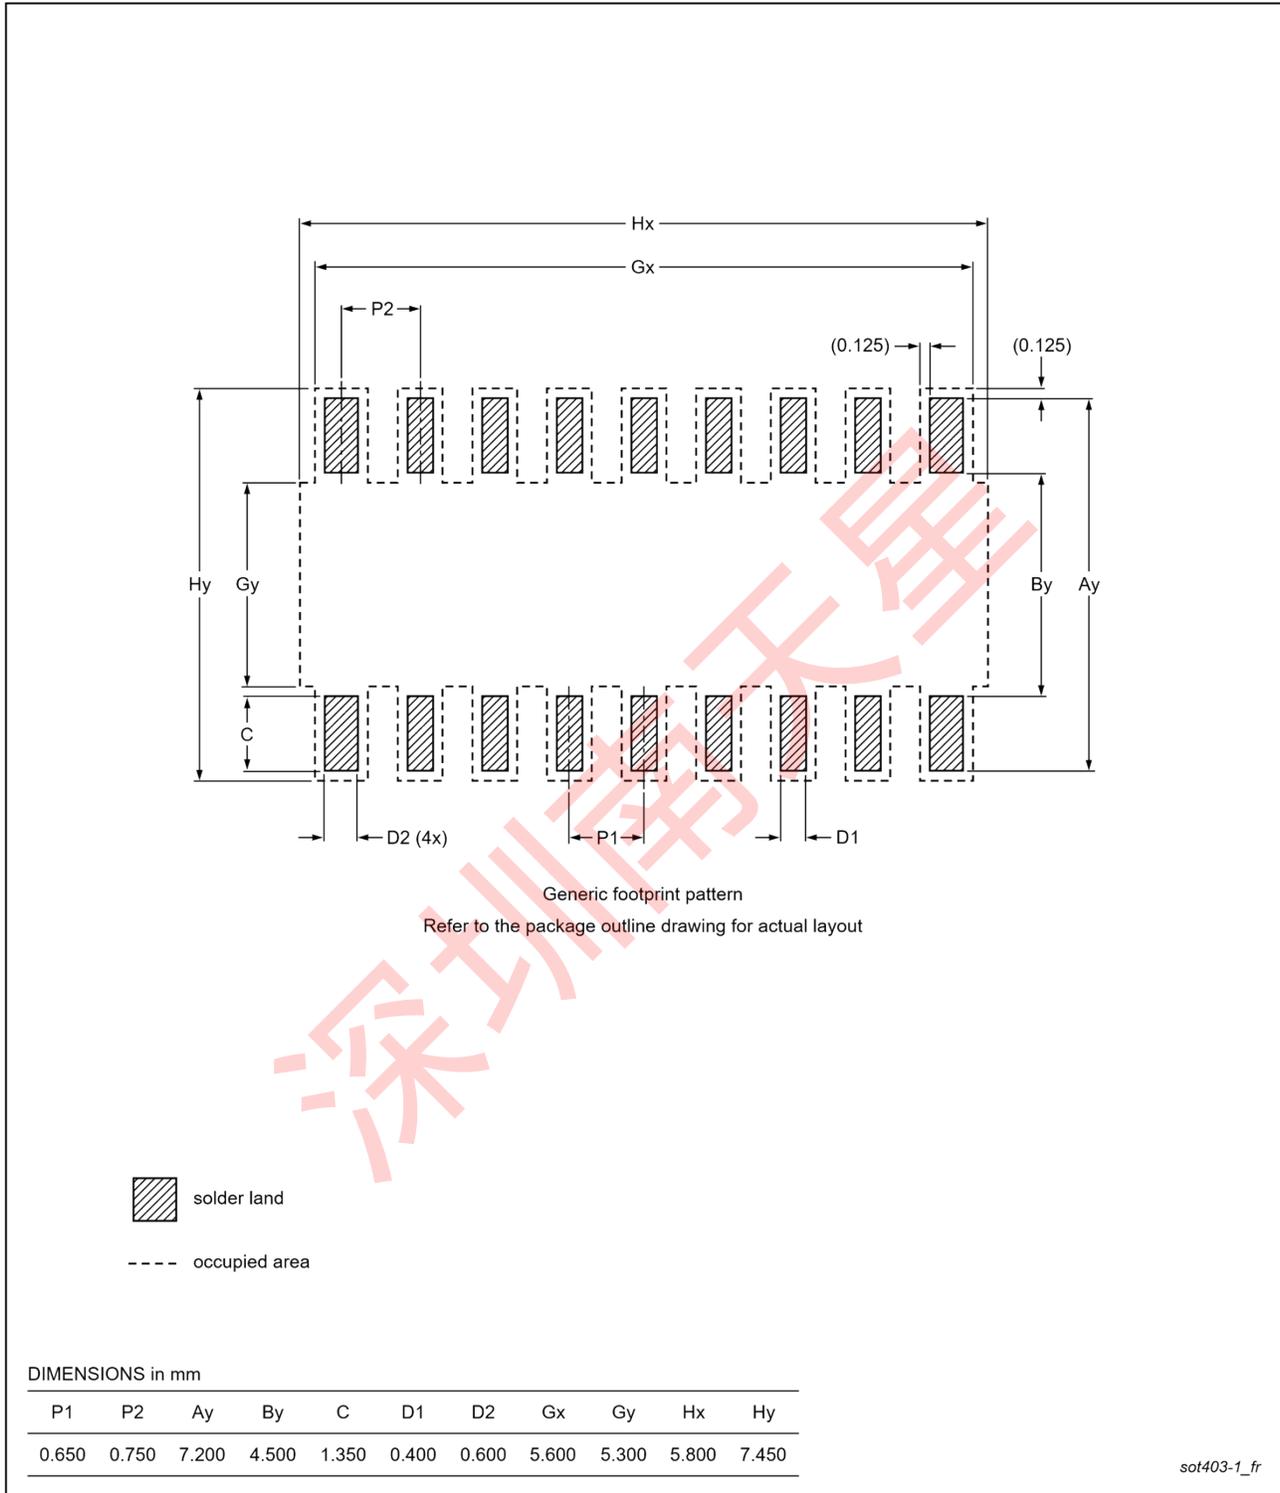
SOT403-1 (TSSOP16) 的 PCB 占地面积; 回流 soldering
